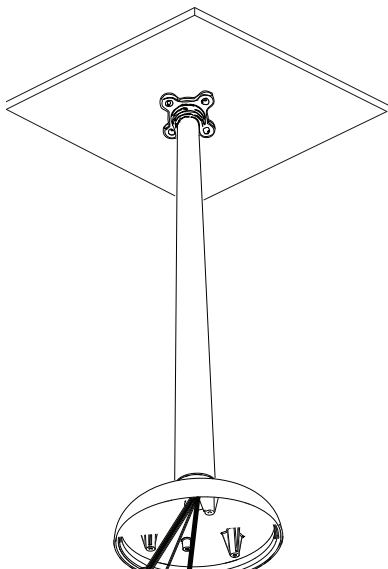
Fixar o suporte pendente para montagem em tubo ao tecto
